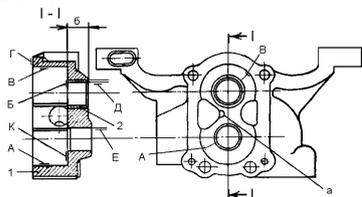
Корпус масляного насоса в сборе со втулкой:
